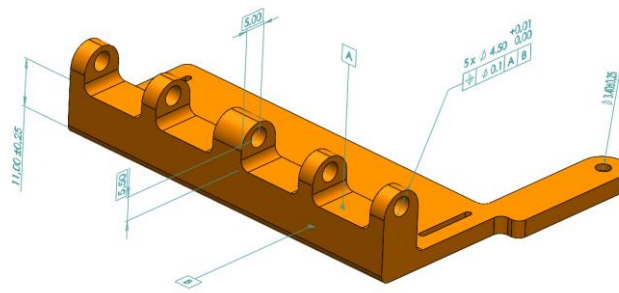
Tolerancias dimensionales “Apoyo mano”
